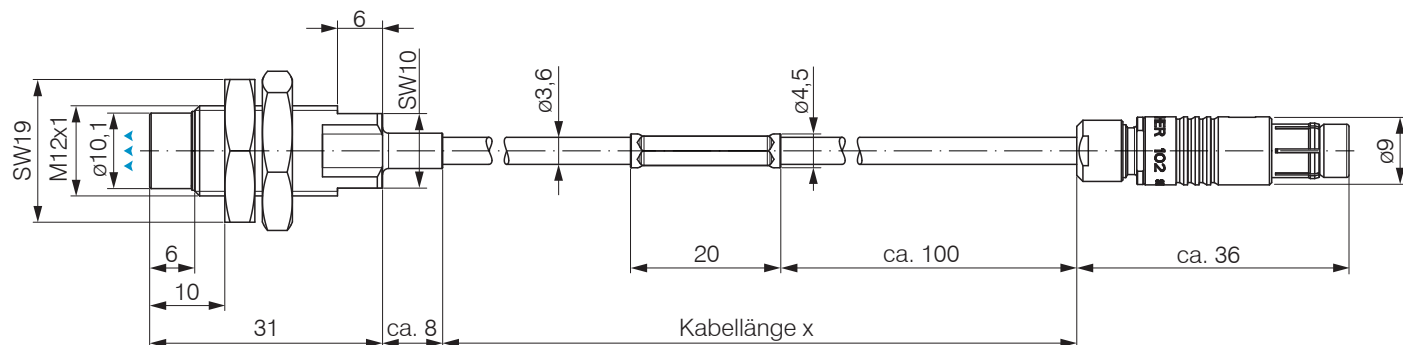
Maßzeichnung Sensoren ES-U3-C-CAx/mB0, Abmessung in mm
